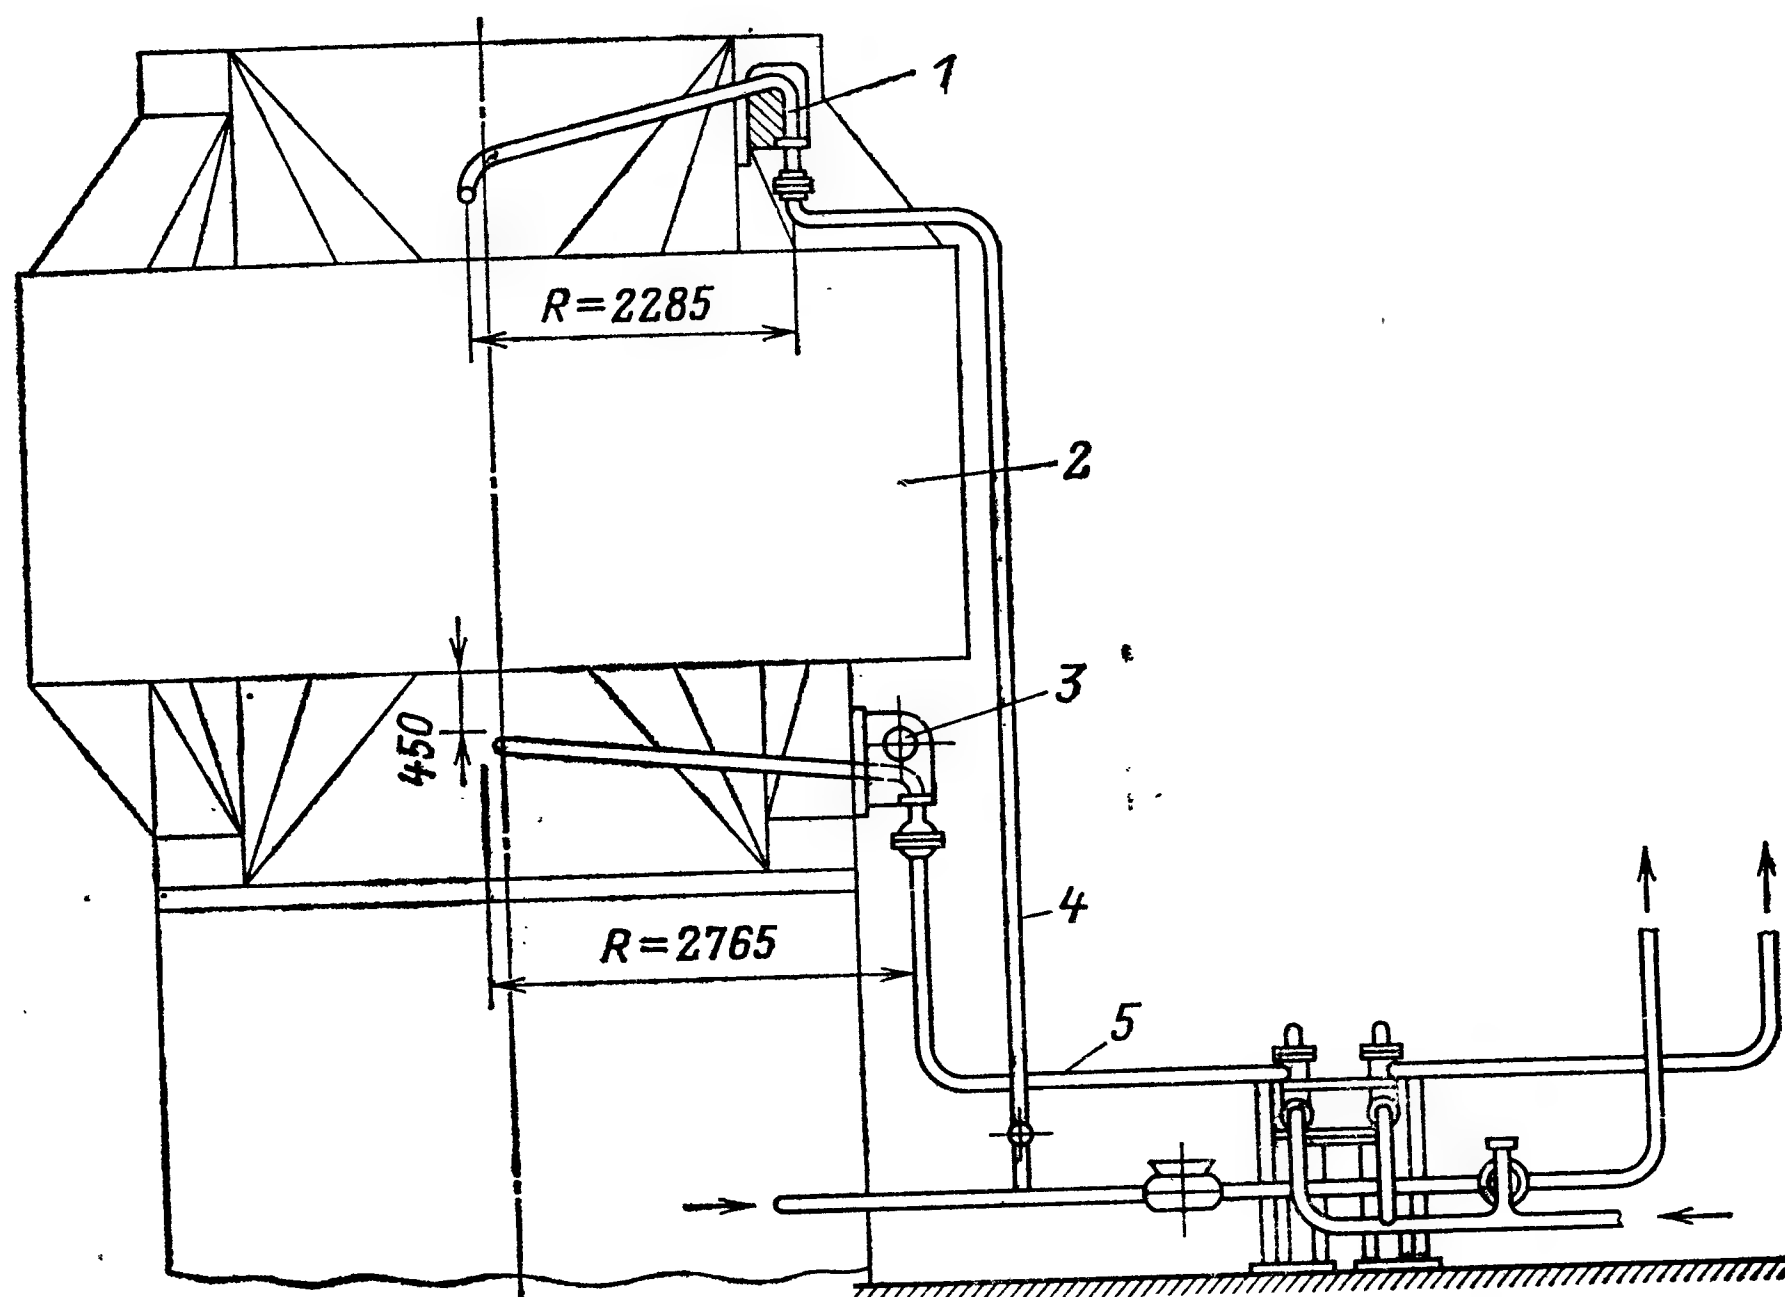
Стационарное устройство для обмывки поверхностей нагрева.
